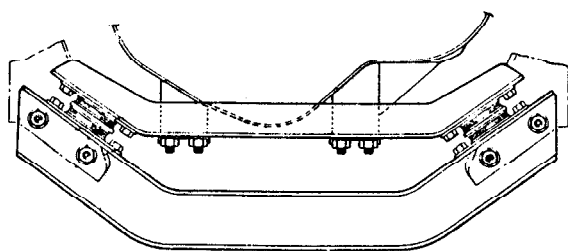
Cojines de caucho en el soporte entre la parte delantera del motor y un travesaño BEDFORD
